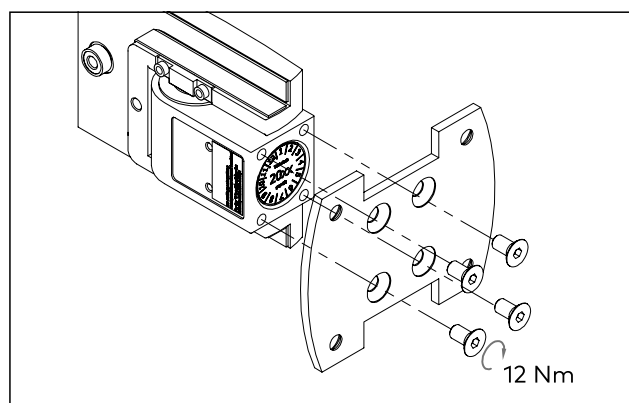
Fissaggio dei pannelli di montaggio sulla cerniera per porta a vento
